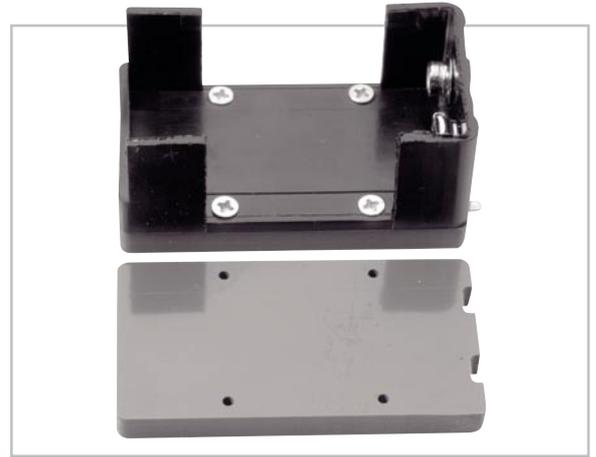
Die Kunststoffplatte für den Batteriehalter (oben)
